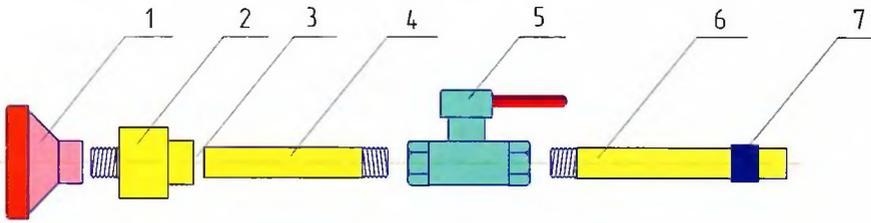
Устройство поливальной насадки: 1 — душевая лейка; 2 — муфта с металлической наружной резьбой; 3 — сварка; 4 — труба полипропиленовая с резьбой; 5 — вентиль; 6 — труба полипропиленовая с резьбой; 7 — изолента ПВХ.
